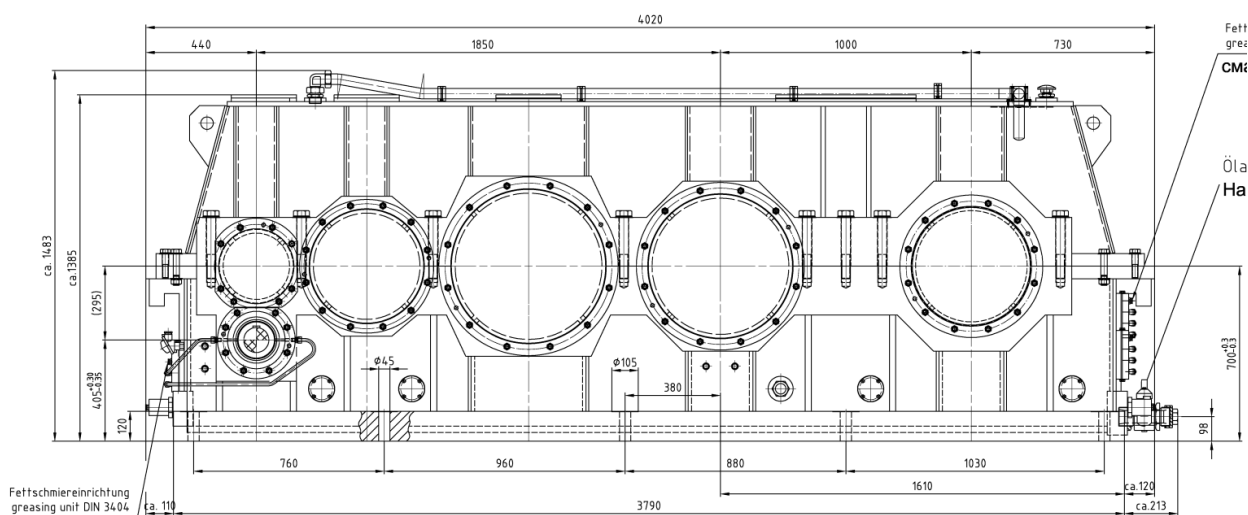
Габаритный чертеж редуктора из руководства по эксплуатации
